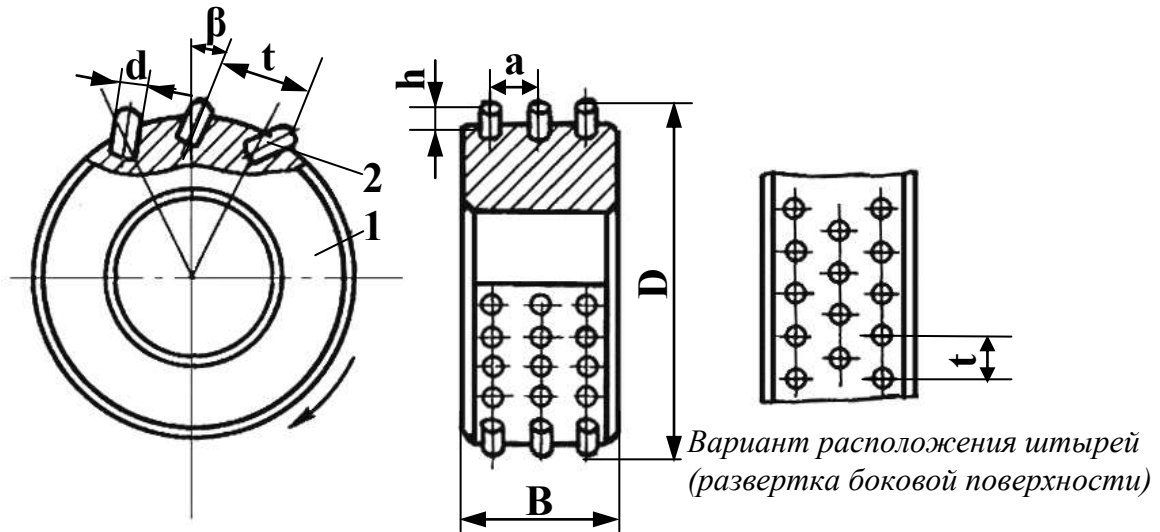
Штыревая шарошка: 1 – корпус; 2 – штырь
